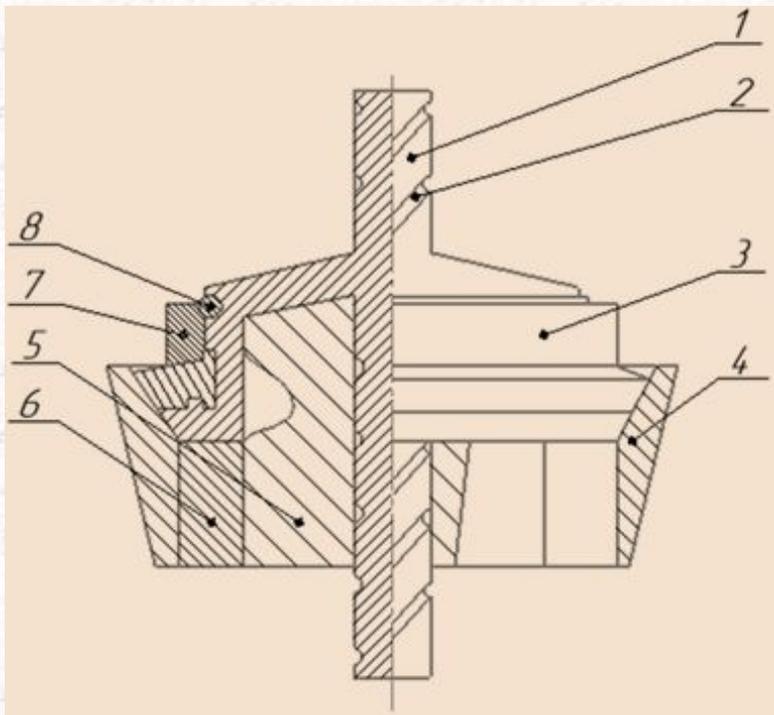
Насосный клапан (1 – шток; 2 – канавка; 3 – корпус; 4 – седло; 5 – стол; 6 – диск; 7 – кольцо; 8 – стопорное кольцо)
